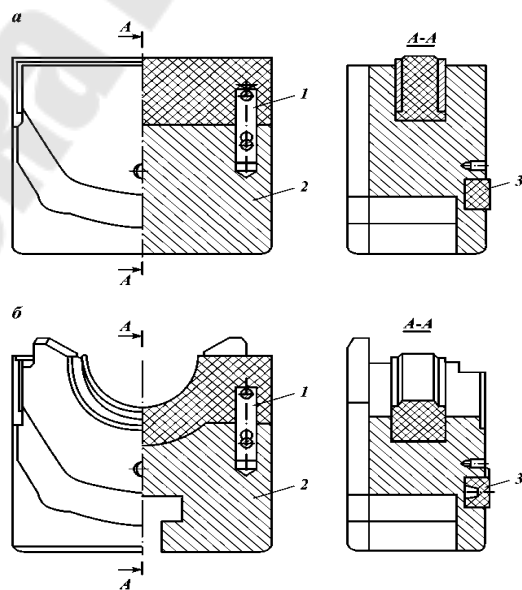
Плашки превенторов ОАО «ВЗБТ»: а – глухая; б – трубная; 1, 3 – уплотнения плашки; 2 – корпус плашки
